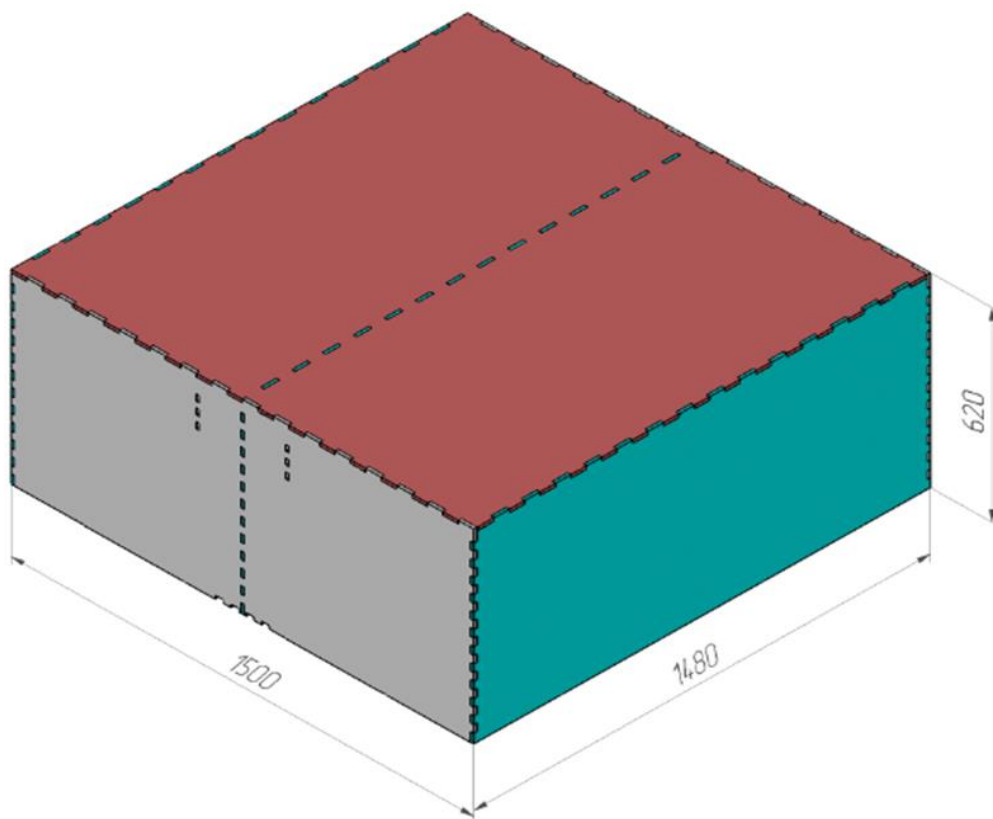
Промежуточная платформа (габаритные размеры)
